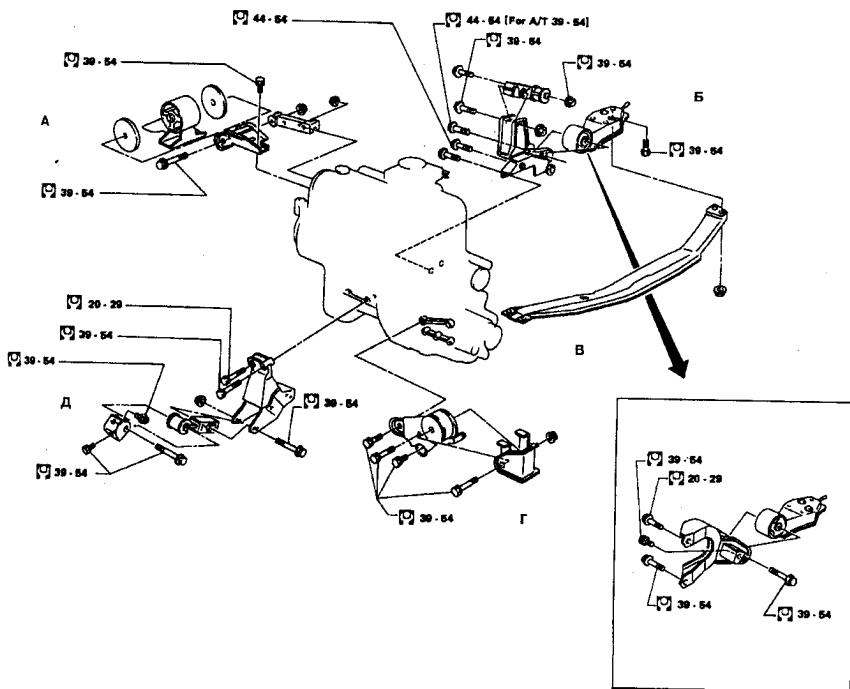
Элементы крепления двигателя и коробки передач (См. Раздел 21)
